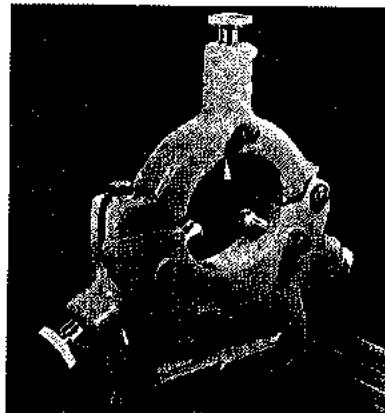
Luneta fija (Monarch Machine Tool Co.).
